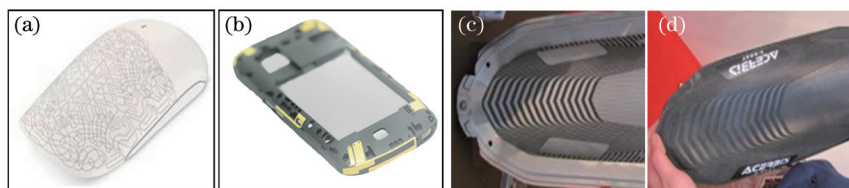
三维曲面的激光加工。(a) 产品曲面打标; (b) 曲面LDS活化; (c) 模具型腔蚀纹; (d) 模具注塑零件
